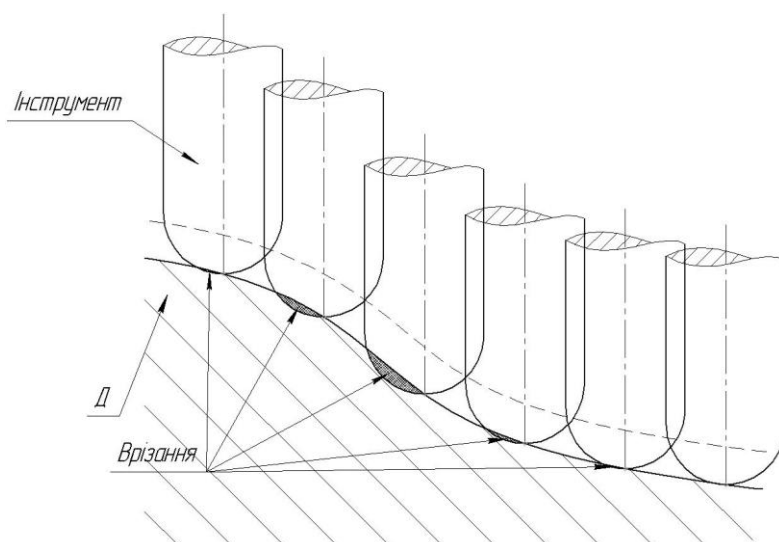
Помилкова схема обробки на 3-ьох координатному фрезерному станку з ЧПК
